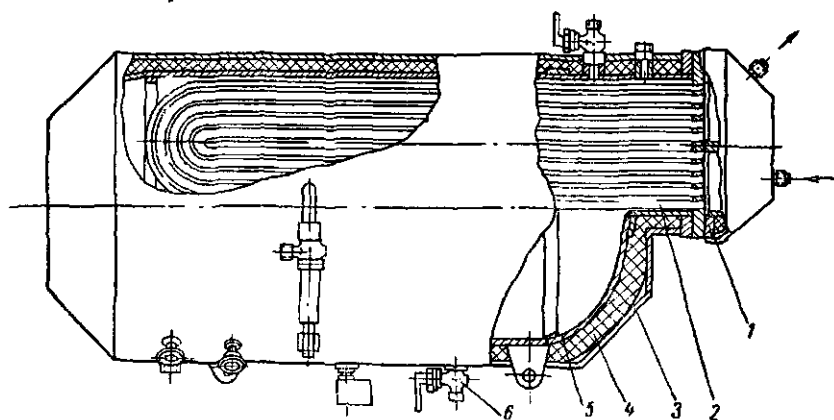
Конструкция водонагревателя бытового емкостного (BCA).
